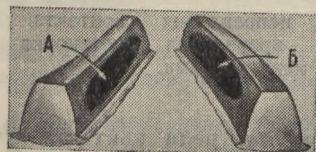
Контакт зуба ведомой шестерни под полной нагрузкой.
